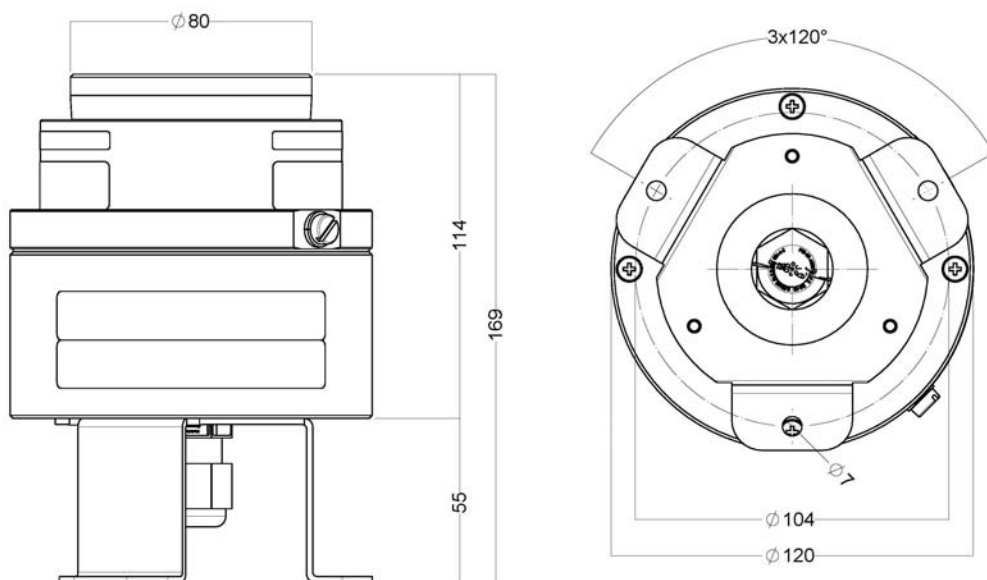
Explosiongeschützte Leuchte Typ HX55, Aufbauvariante
